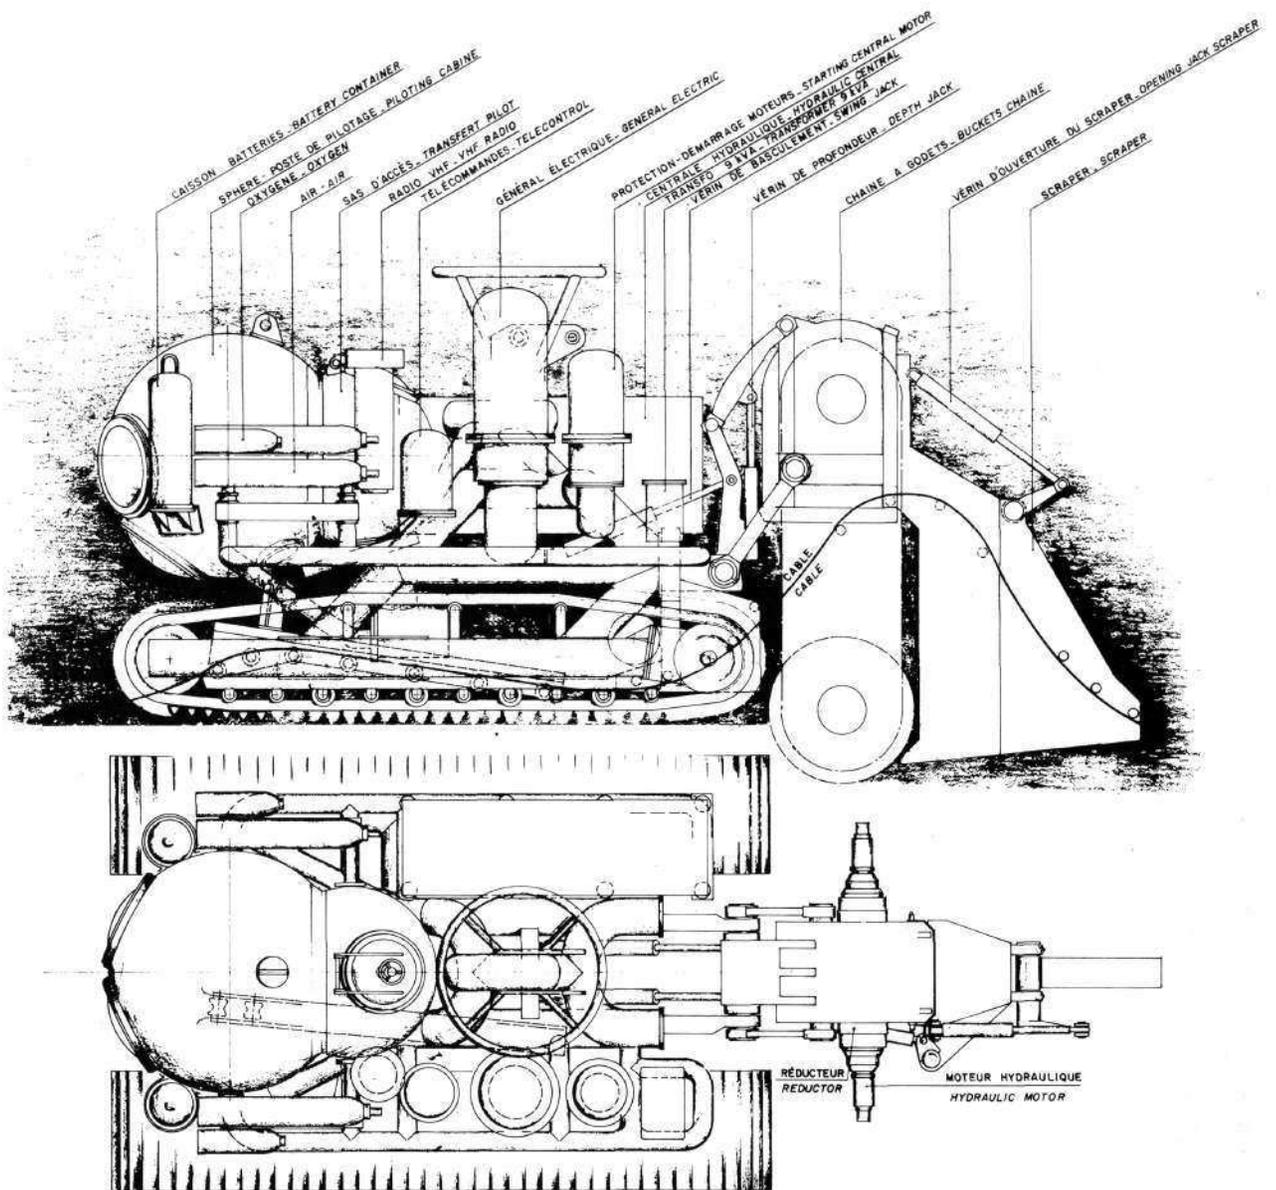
ENSUILLEUSE - VUE D'ENSEMBLE
